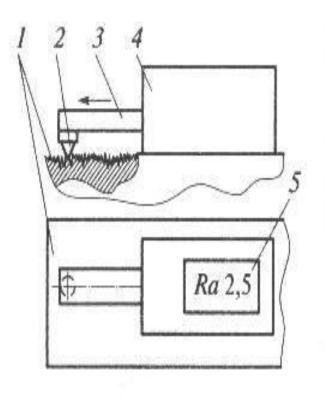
Измерение шероховатости поверхности с помощью малогабаритного накладного профилометра:
